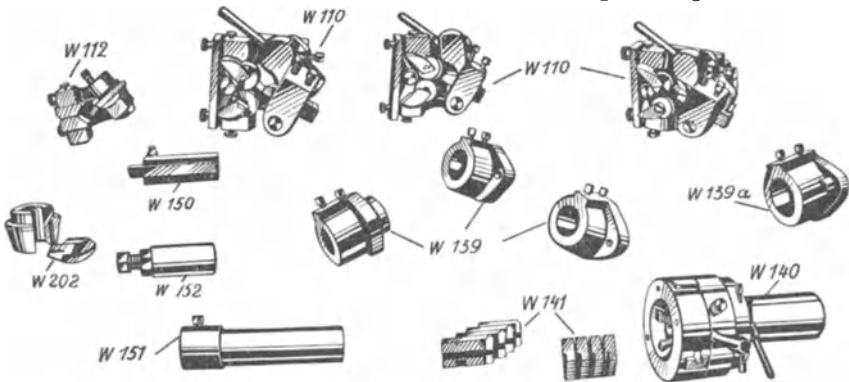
Stangenwerkzeuge für Revolverbänke.
